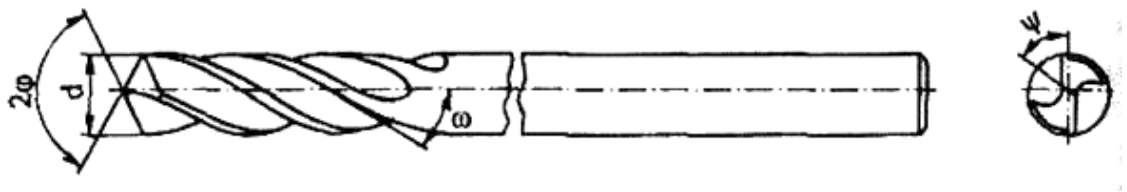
Ескіз свердла спірального для обробки отвору
